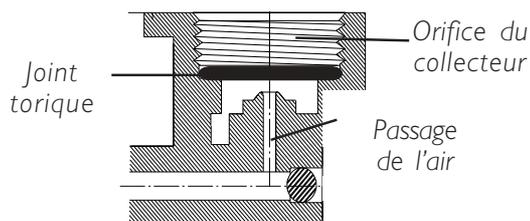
DEMONTAGE/INSTALLATION DES JOINTS TORIQUES
